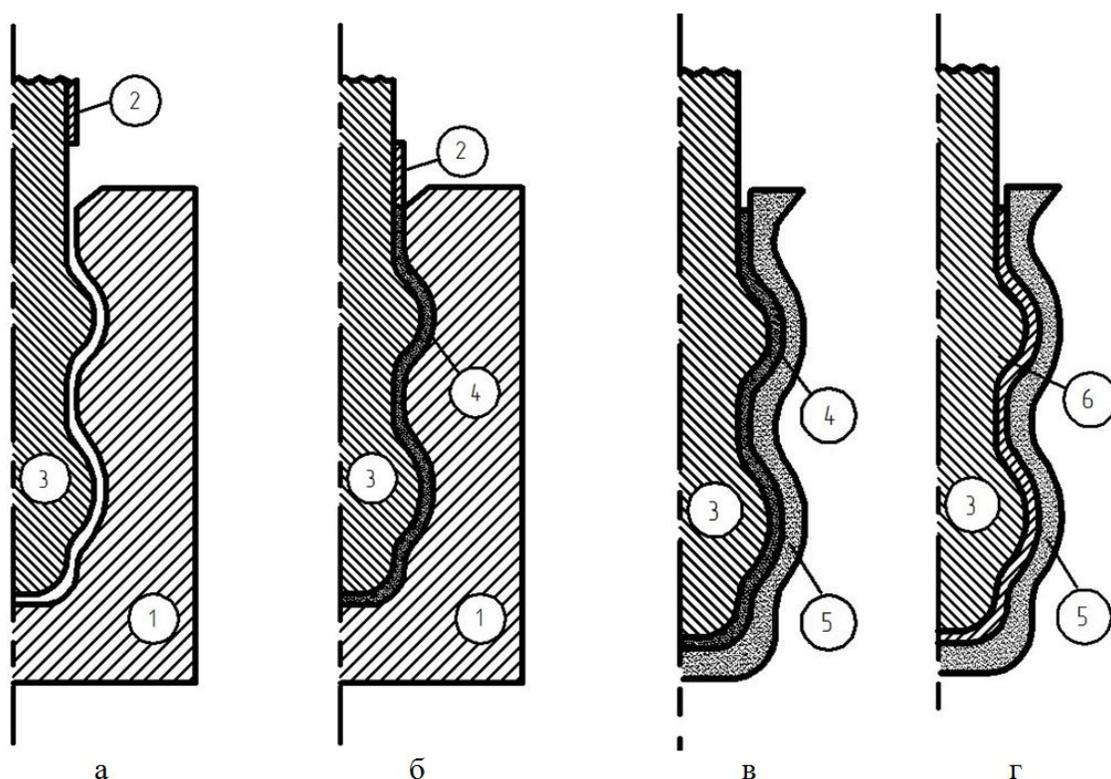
Схема последовательности формирования биметаллической отливки: 1 – пресс-форма; 2 – подвижный пресс-пуансон; 3 – стальной каркас; 4 – воскообразный напрессованный слой; 5 – керамическая оболочка; 6 – биметаллическая отливка в оболочковой форме.
